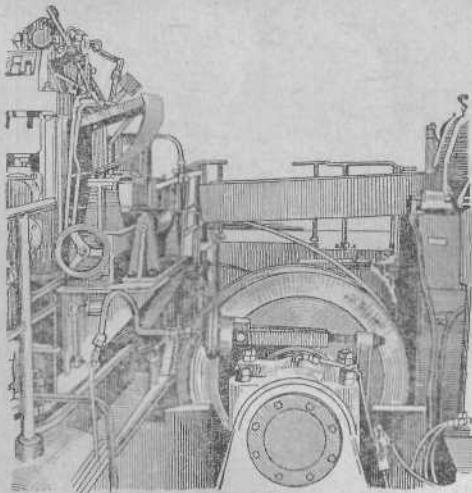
Положение рулона на второй позиции разматывателя профилегибочного агрегата 2-7×80-500.
